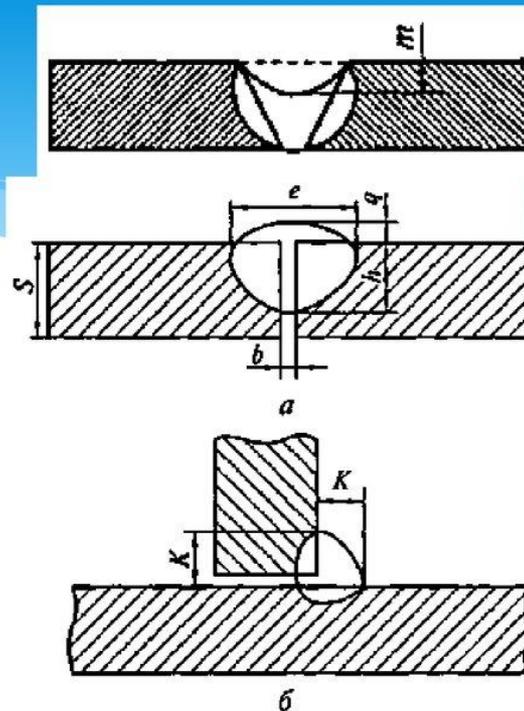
Основные геометрические параметры сварных швов (по ГОСТ 2601—84):
